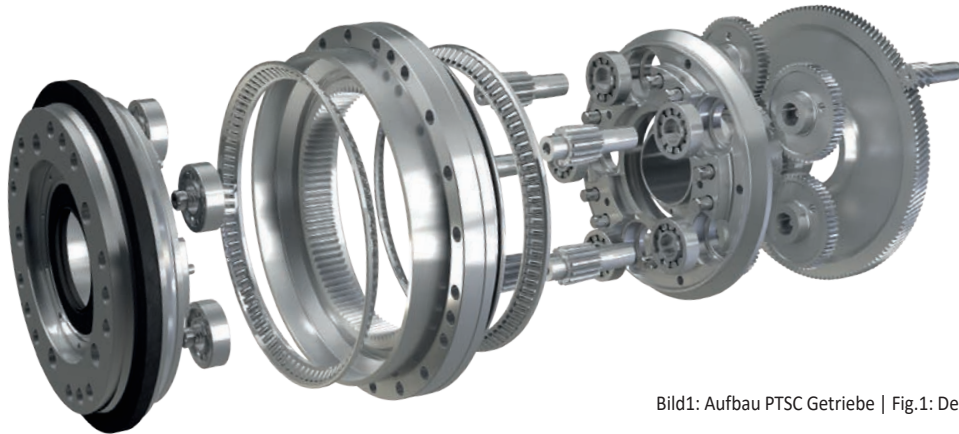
Aufbau PTSC Getriebe | Fig.1: Design PTSC gear box
